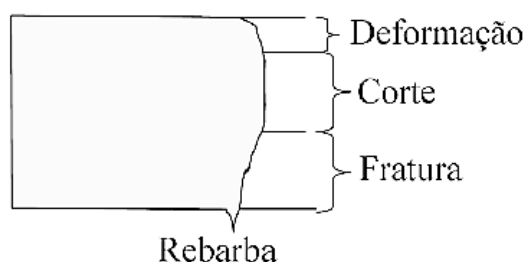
Aspeto de uma aresta guilhotinada. [4]
